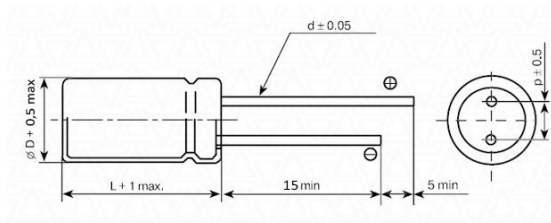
Габаритні розміри конденсатора К50-35
